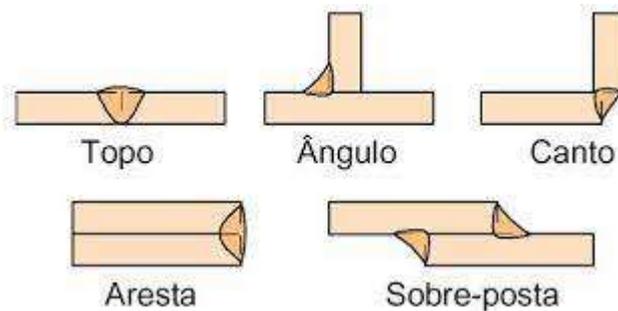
Alguns tipos de junta para soldagem com eletrodo revestido.
